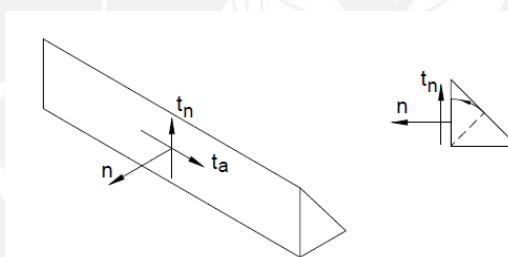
esfuerzos en el filete de soldadura.
